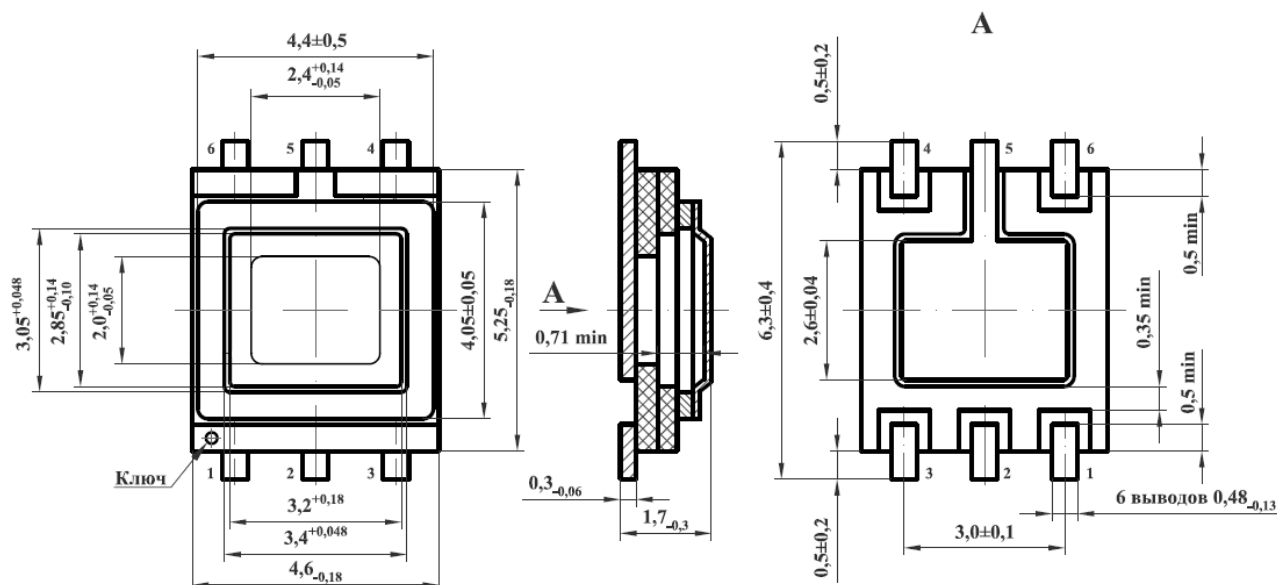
Габаритный чертеж корпуса 5221.6-1 (размеры в мм)
